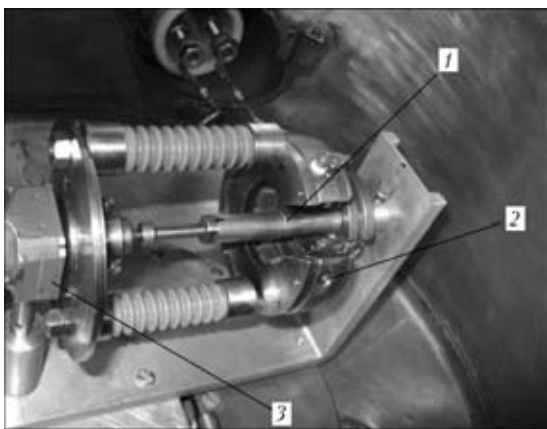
Опытный образец электронно-лучевого нагревателя для орбитальной ЭЛС стыковых соединений труб: 1 — свариваемый образец; 2 — кольцевой электронно-лучевой нагреватель; 3 — привод орбитального вращения
